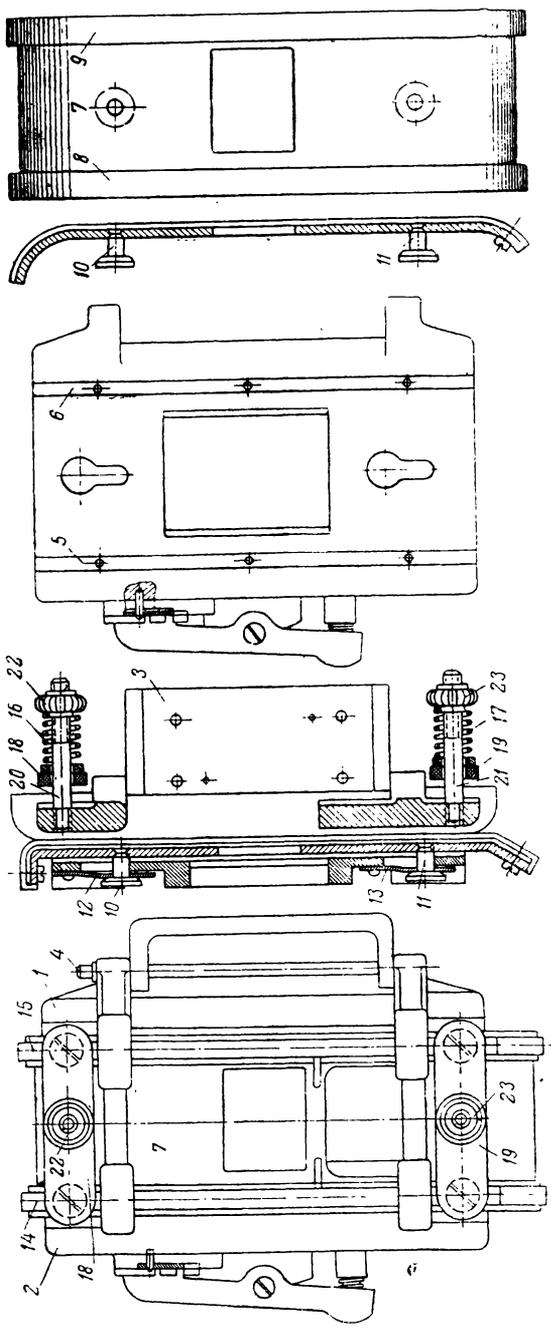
Фильмовый канал кинопроектора К-101 и его детали
